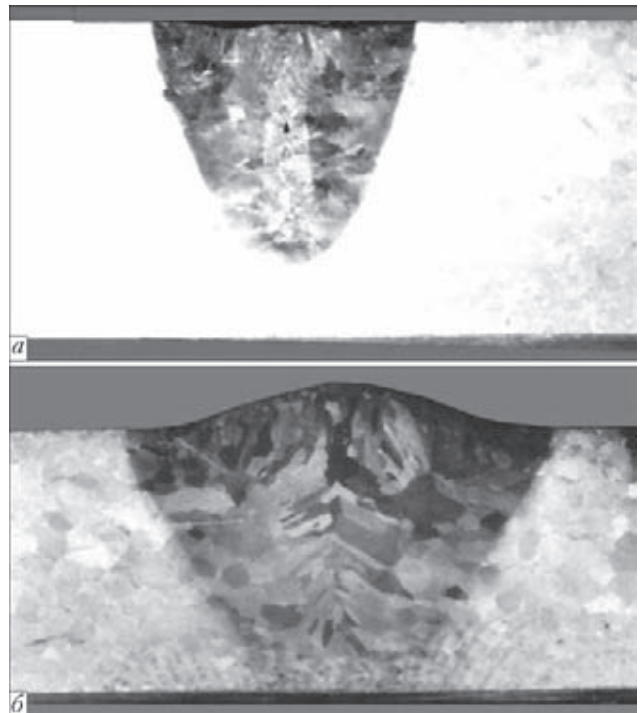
Поперечные макрошлифы швов титанового сплава Т110 толщиной 13 мм, выполненные лазерной (а) и лазерно-дуговой сваркой (б) при одинаковой мощности лазерного луча
